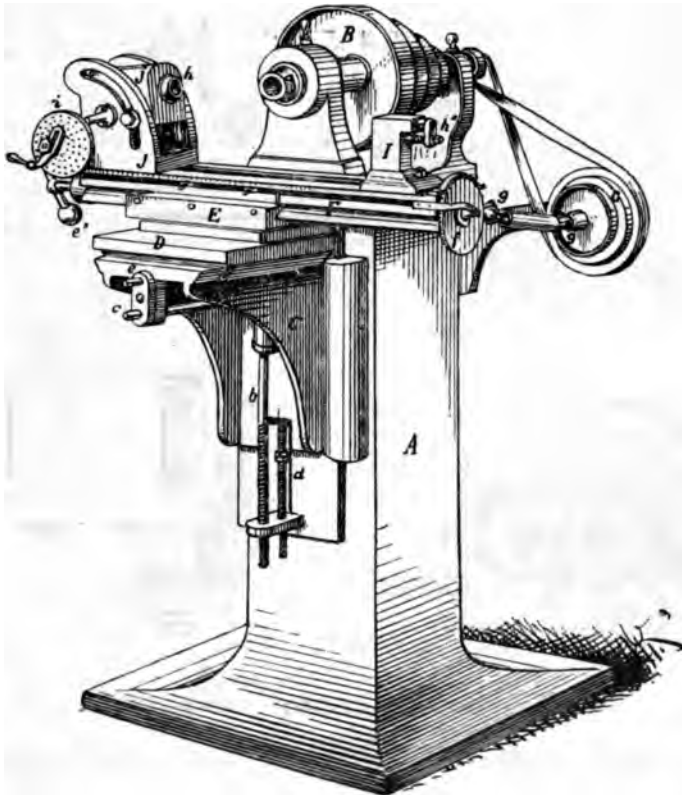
Universalfräsmaschine von Brown & Sharpe.
